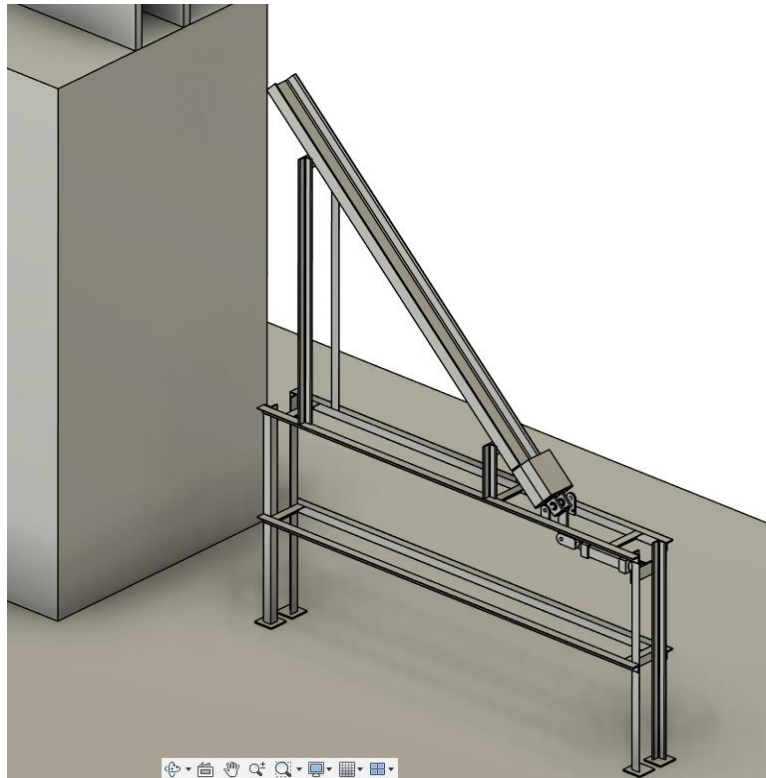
Vista final en perspectiva del conjunto posicionador de trozos
